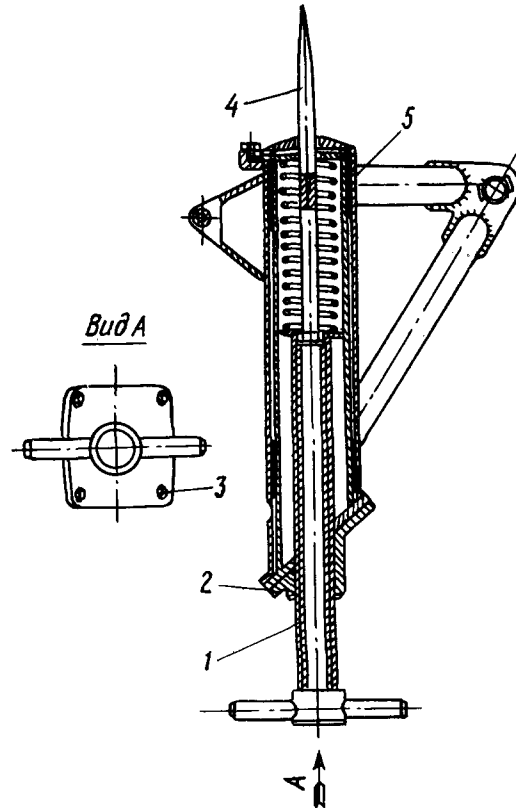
Приспособление для сборки шкворня с фермой:
